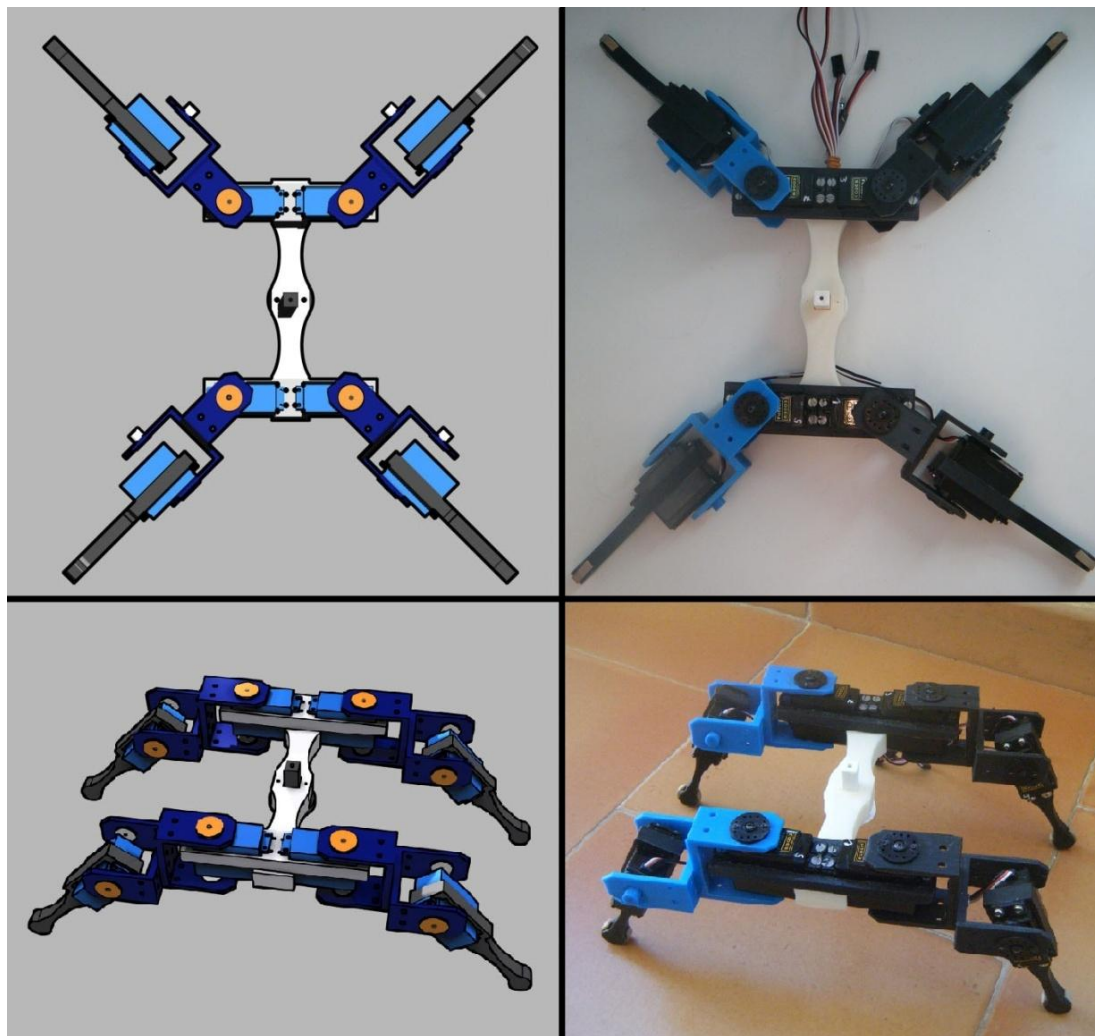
Vista del montaje completo de todas las piezas impresas junto a los servos
